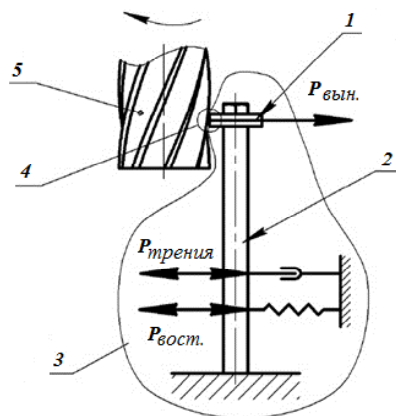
Схема стэнда для вивчення процесу фрезерування деталей з різною жорсткістю: 1 – оброблюваний образец; 2 – пружна пластина; 3 – пружна система деталь – приспособление; 4 – зона різання; 5 – кінцева фреза
